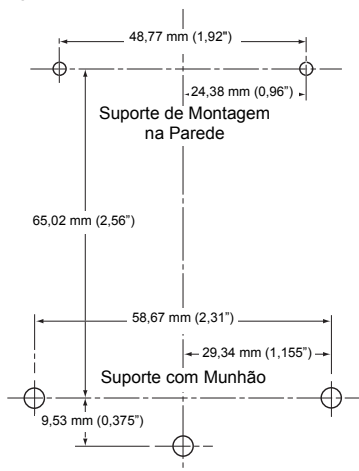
Dimensões para Instalação Dupla de Suporte com Munhão e Suporte de Montagem na Parede
